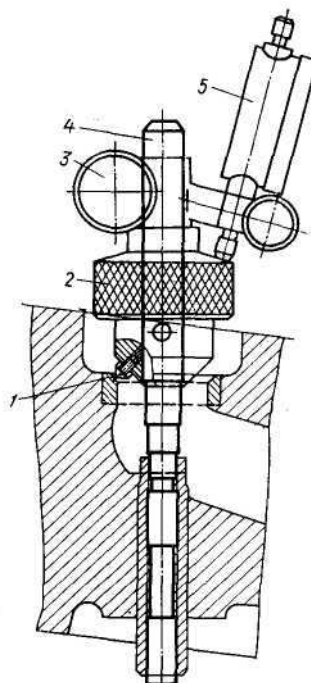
Приспособление для проверки concentричности фаски седла клапана оси направляющей втулки:
